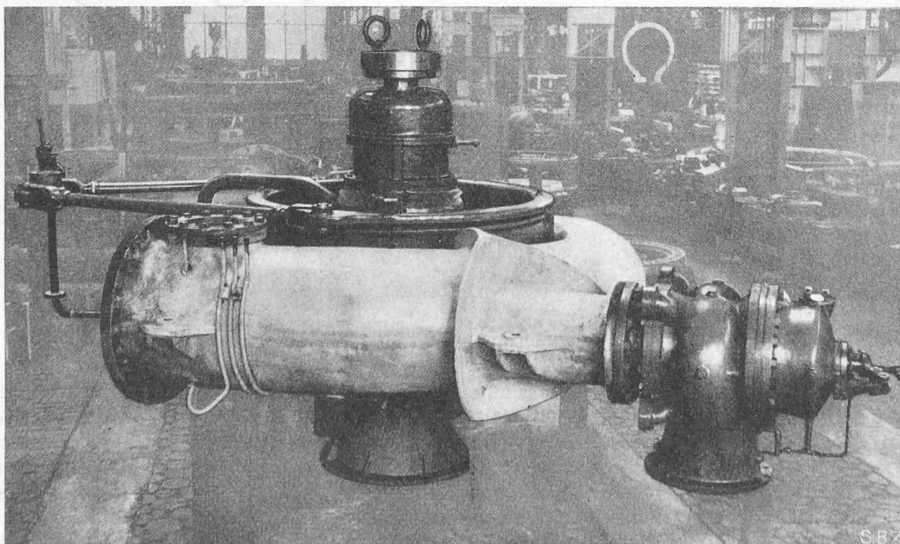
Plessurturbine mit angebaubem Druckregler (rechts vorn), Leitungsverstellung und Belüftungsventil (links)
